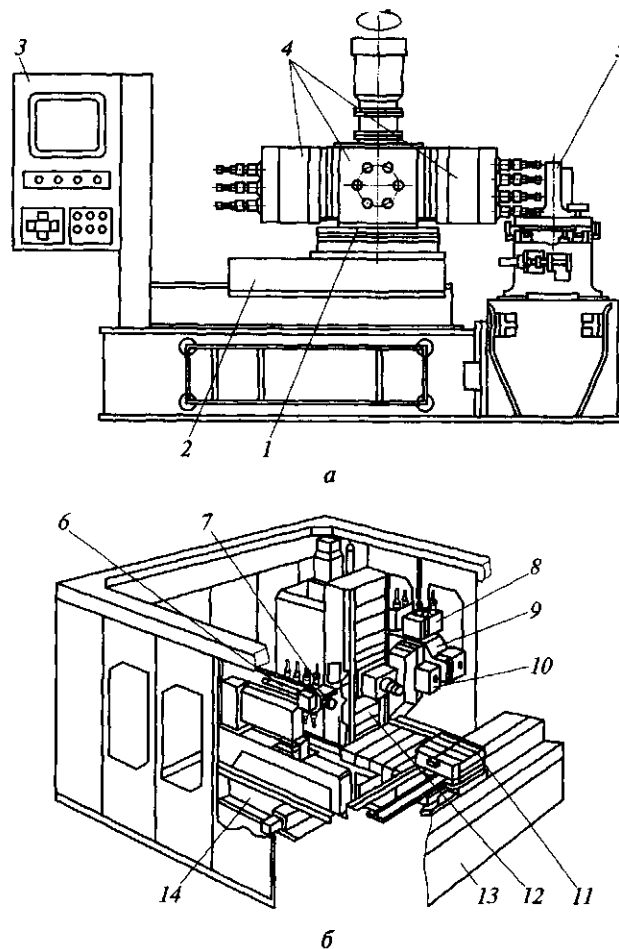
Агрегатные станки с ЧПУ со сменными шпиндельными коробками (*а*) и с магазином шпиндельных коробок (*б*):
